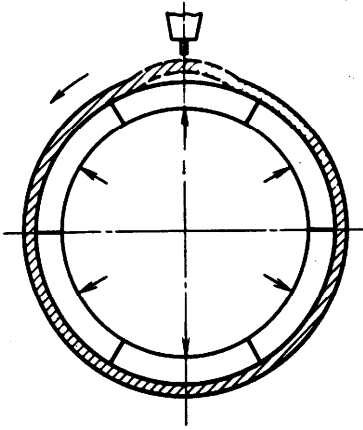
Схема подъема кромок при сварке кольцевого стыка на разжимной оправке
